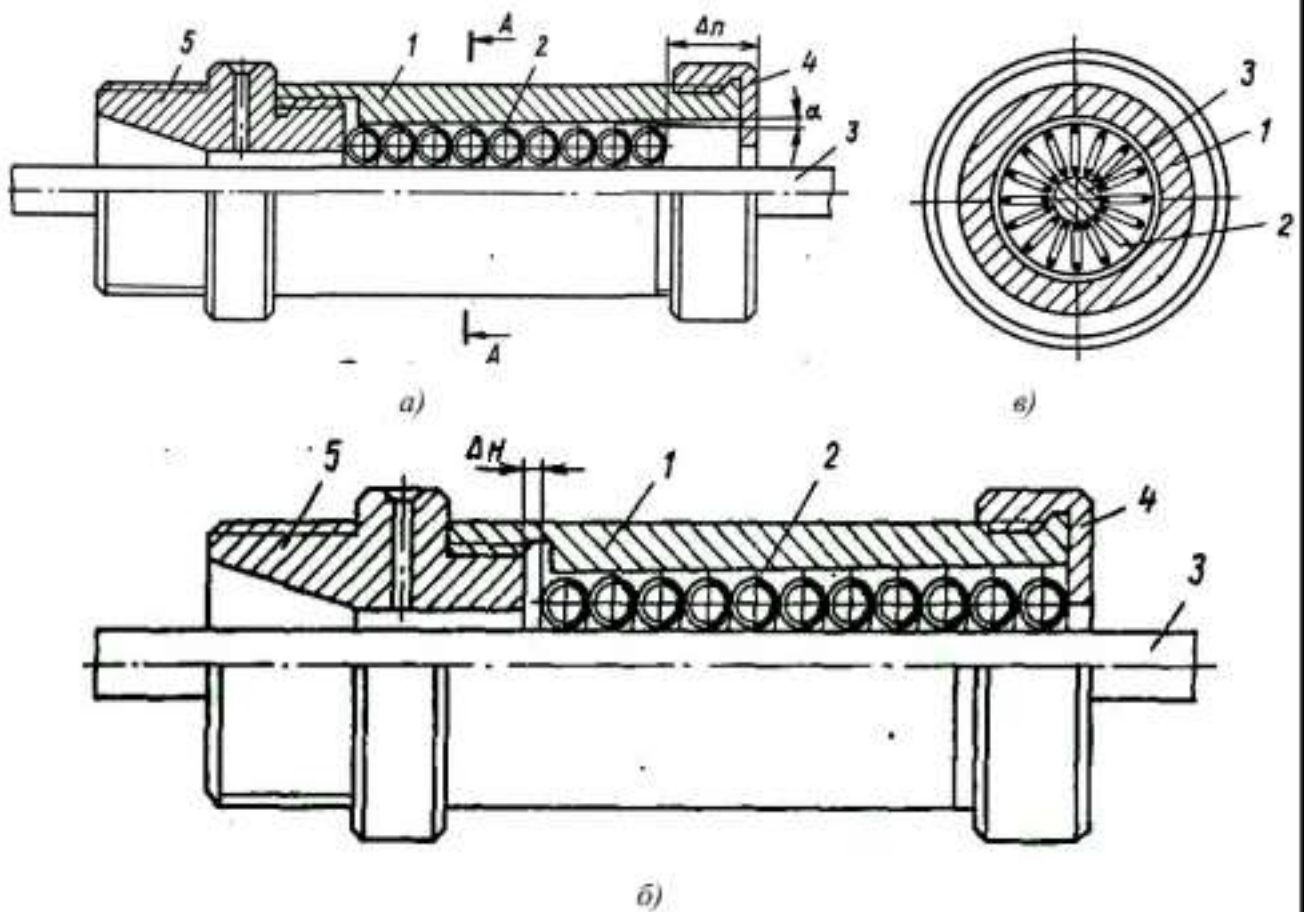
Подаюча цанга кращої довговічності: а- для подачі заготовки; б- для наборі пруткової заготовки; в- поперечний переріз А-А
